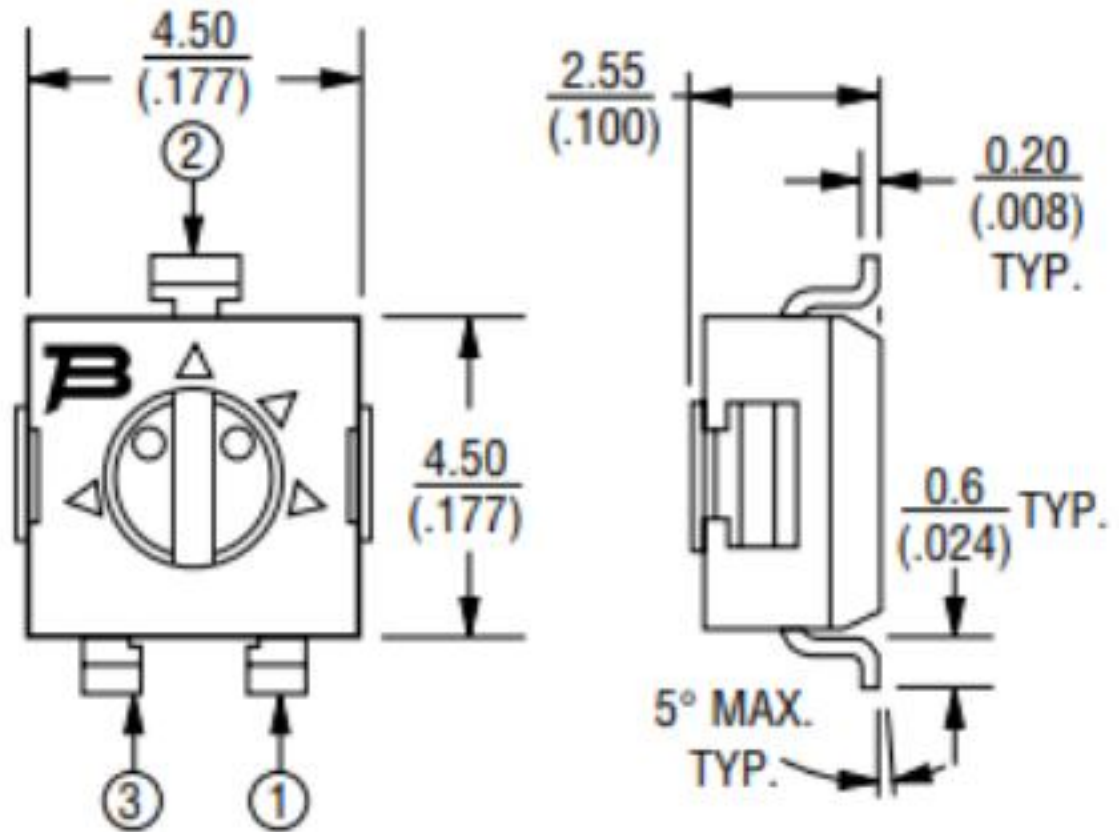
Габаритні розміри підстроювального резистора 3314G-1-103E
